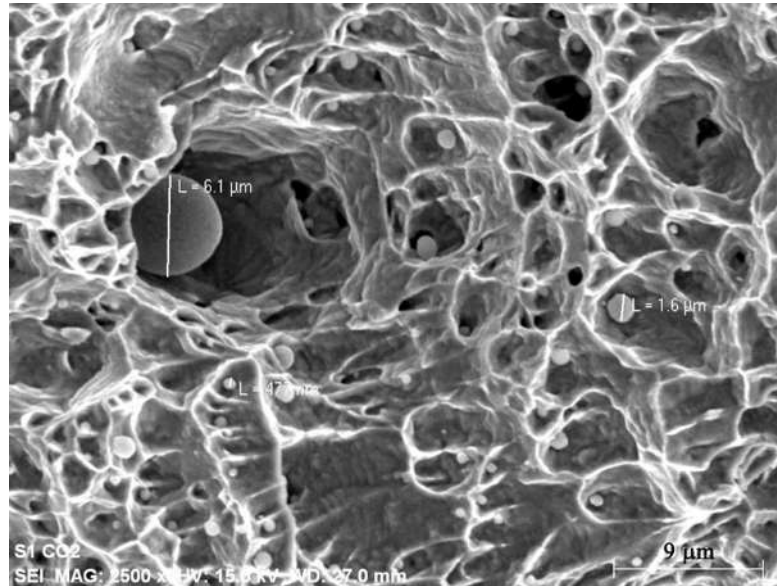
Tamaño de inclusiones en la unión soldada con 100% CO₂.
